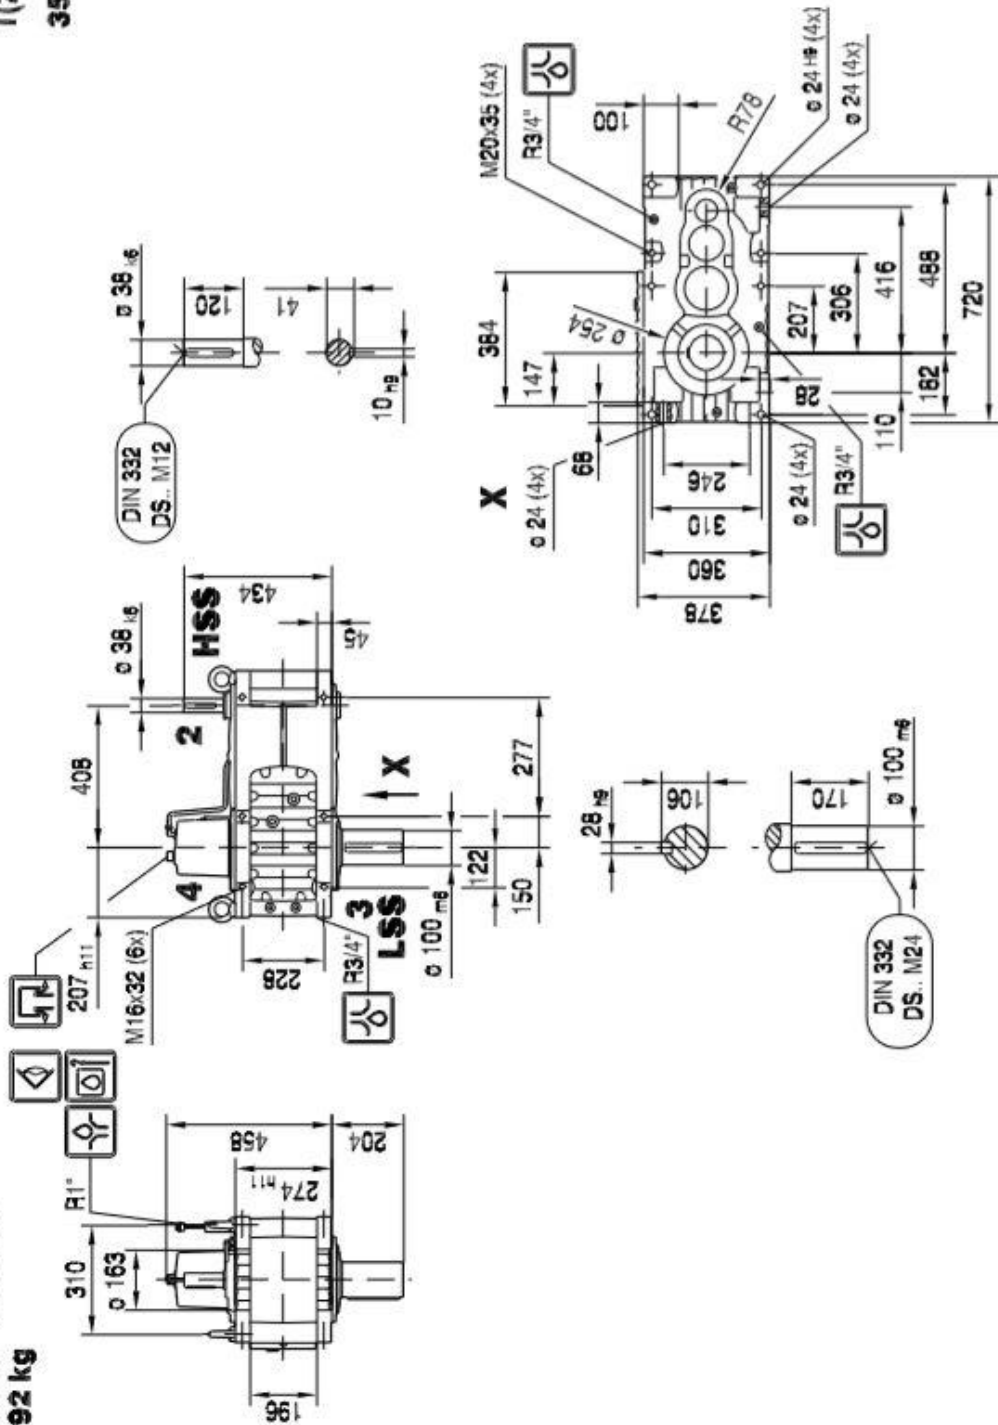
Desenho técnico do redutor MC3PVSF03 [49]
